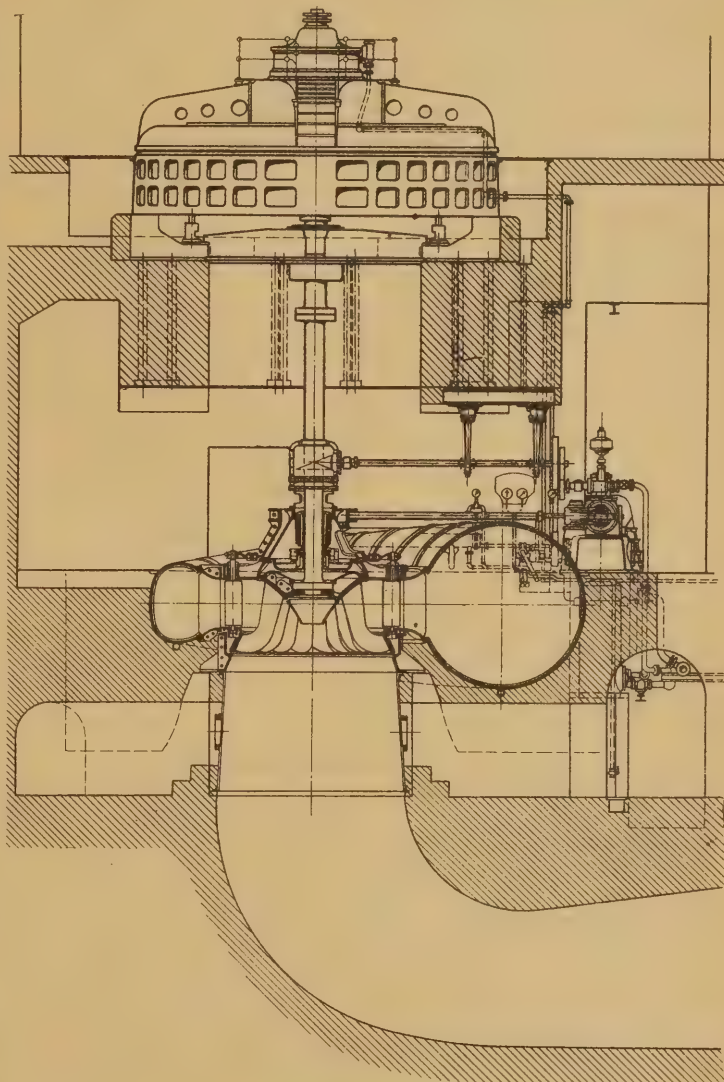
12500 PS-Maschinensatz des Omine-Kraftwerkes mit Schnitt durch die Spiralturbine und Ansicht der Schirmdynamo.
